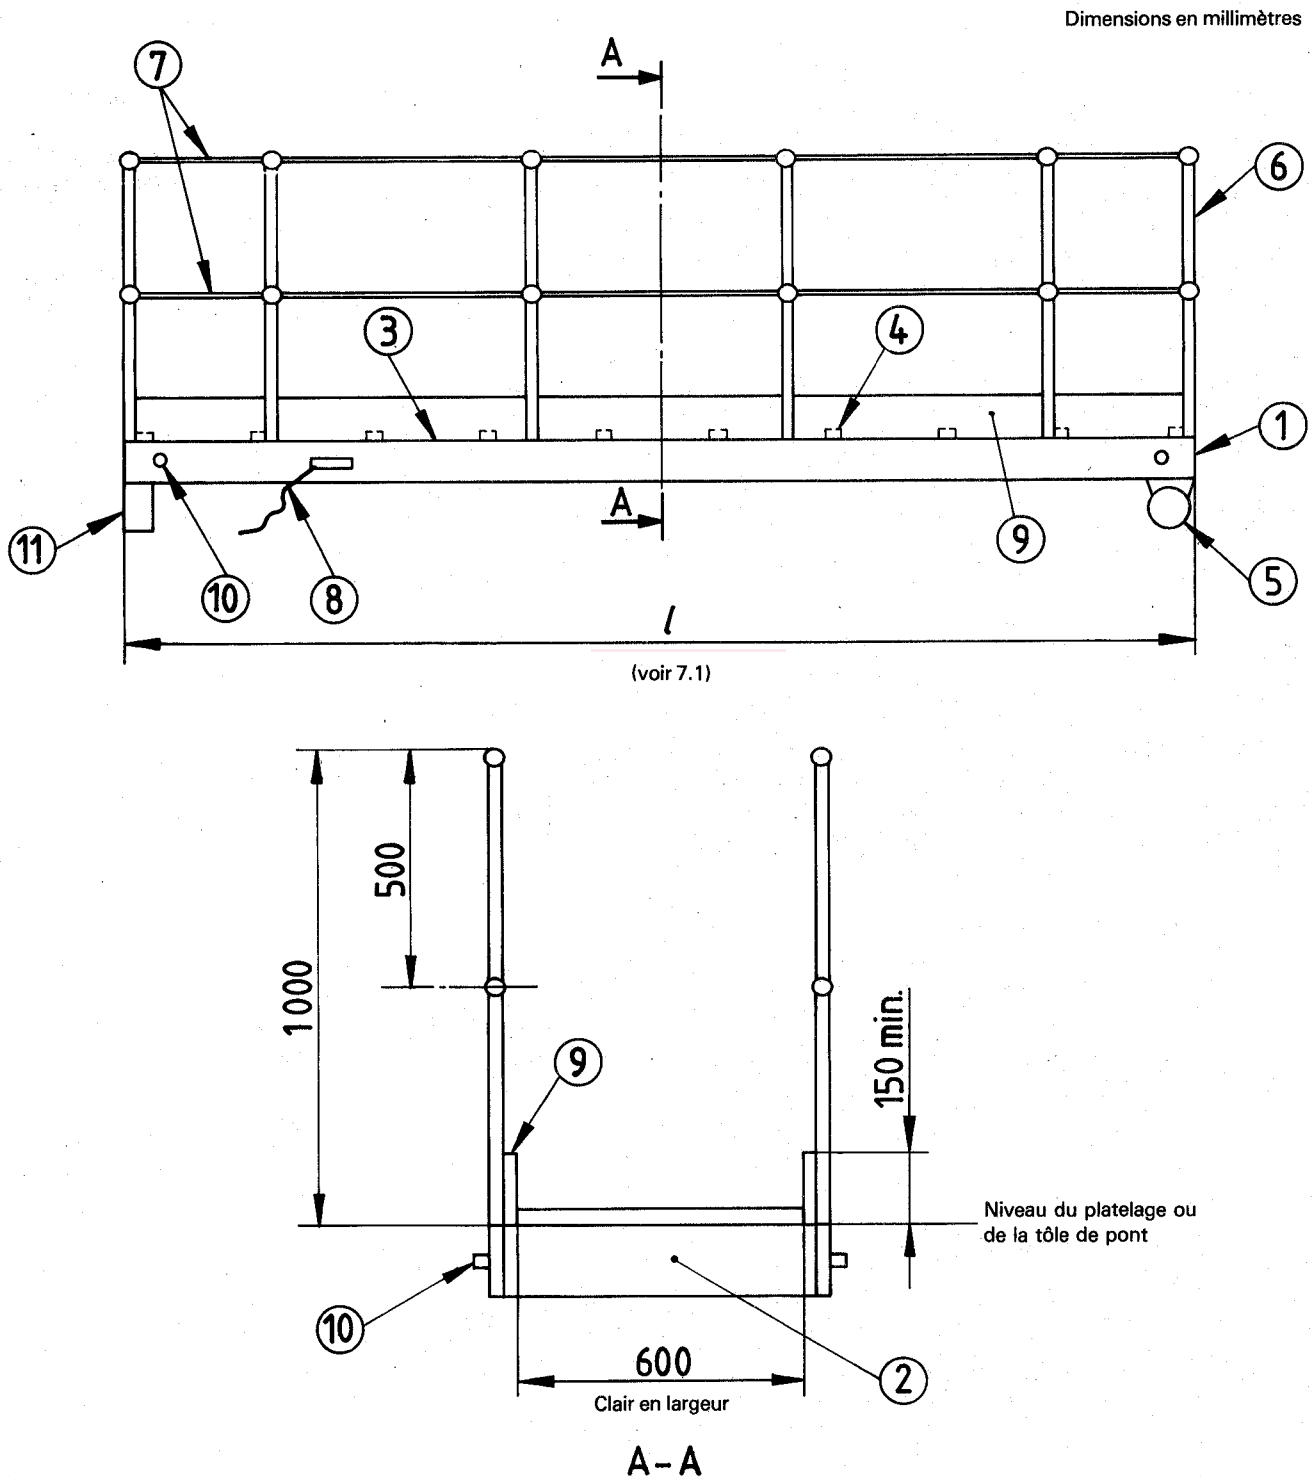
Disposition générale d'un planchon de type A (voir le tableau pour les numéros de référence)
